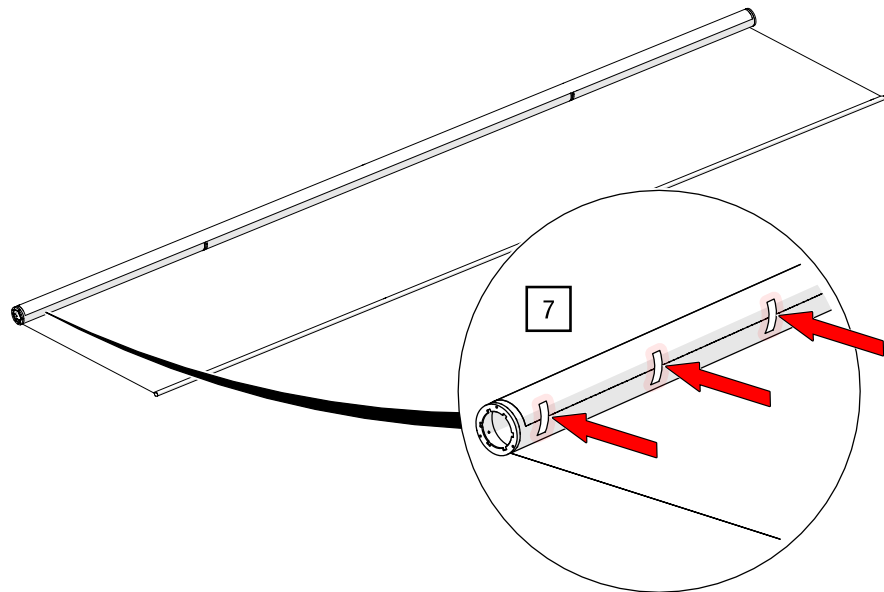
Behang Montieren – Behang mit Klebeband fixieren
